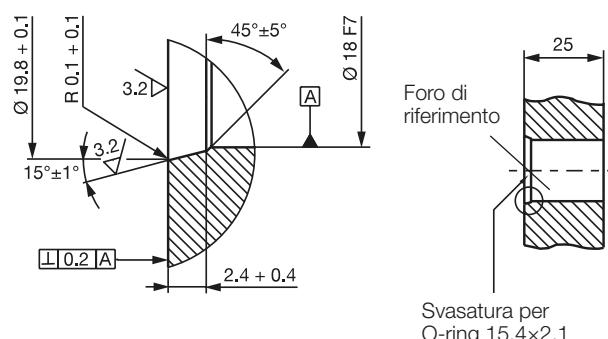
Foro di riferimento per il montaggio del BTL con l'O-ring
